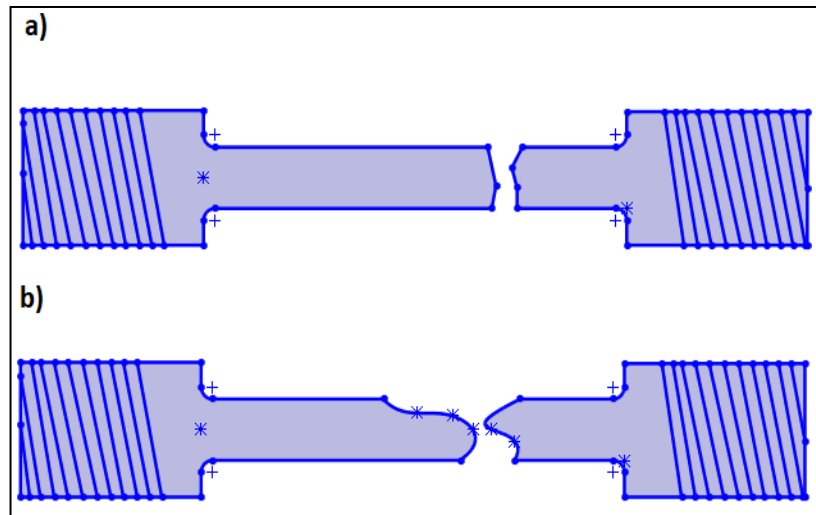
a) Fractura en materiales frágiles, b) Fractura en materiales dúctiles [7].
